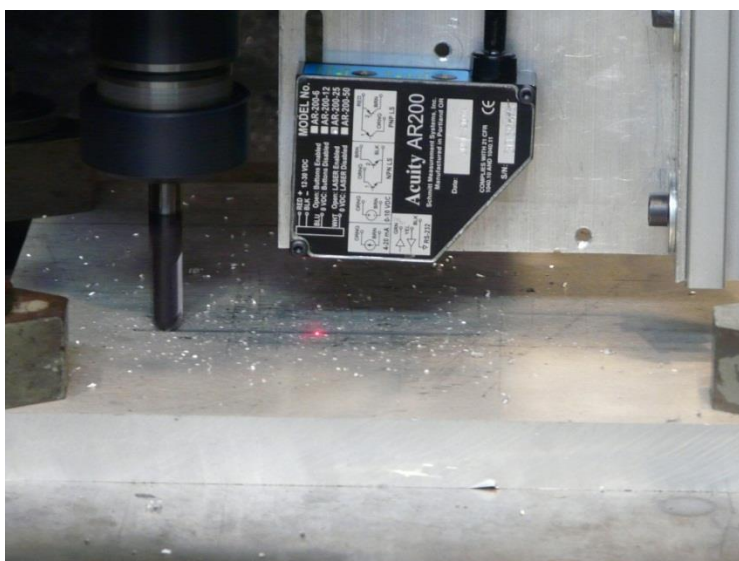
Montaje de ensayos de medición del espesor con un sensor láser
